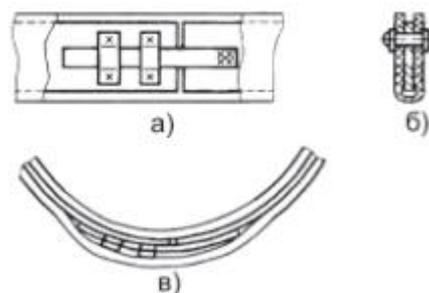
Приспособление (уплотняющее кольцо) для накачки бескамерной шины
